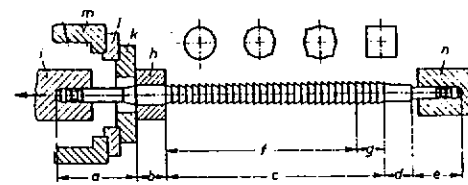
Aguja de brochar en posición de trabajo. a) Mango; b) guía de entrada; c) dentado; d) guía; e) extremo; f) parte de corte; g) parte de calibrar; h) pieza a mecanizar; i) pieza portátil; k) apoyo; l) placa de sujeción; m) cuerpo de la máquina; n) soporte de acompañamiento.
